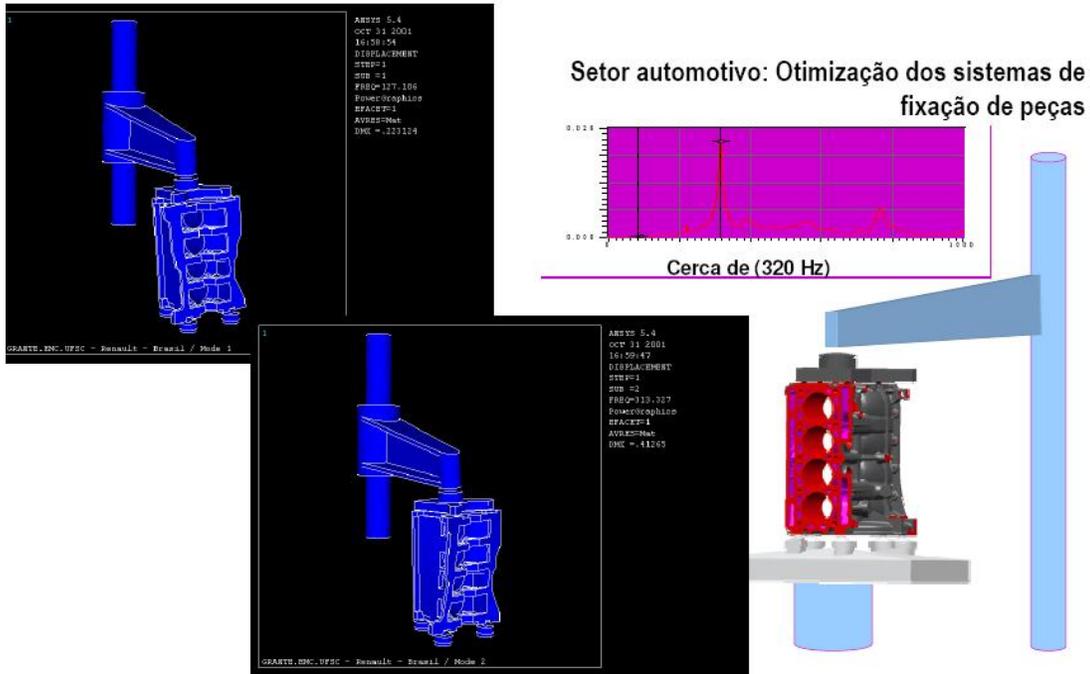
Estudo de caso da usinagem de bloco de motor realizada pelo CCM
